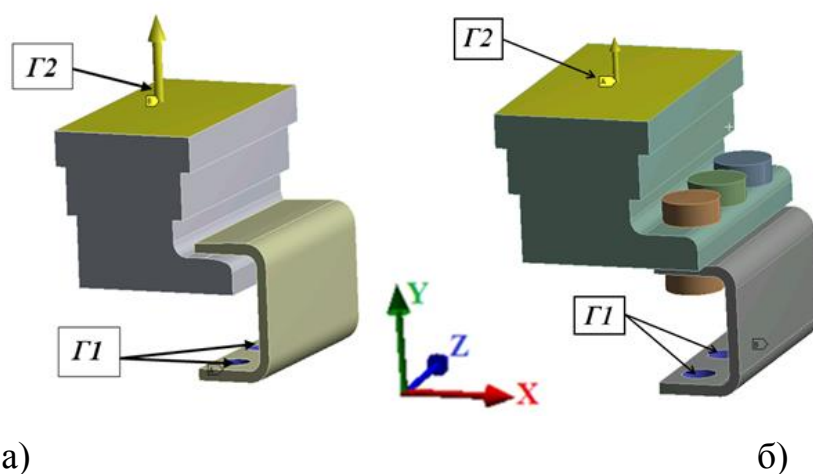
Схема граничных условий для первой (а) и второй (б) расчетной схемы испытаний сегмента шпангоута; $\Gamma 1$ - площадка жесткого закрепления заднего фланца, $\Gamma 2$ – площадка задания перемещений по оси Y
